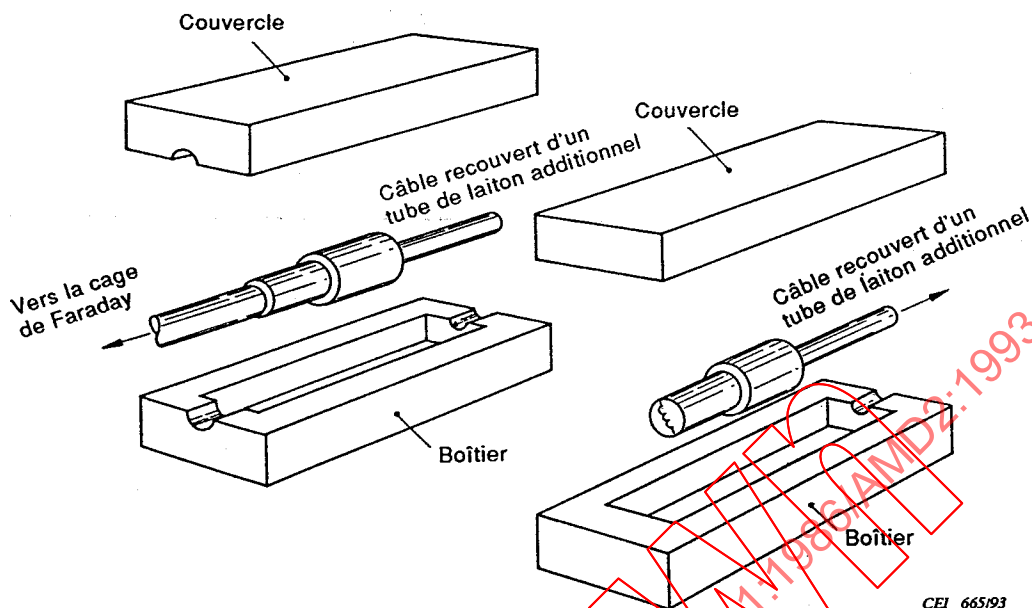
(A.5.6) - Ecran additionnel des connecteurs du câble en essai
